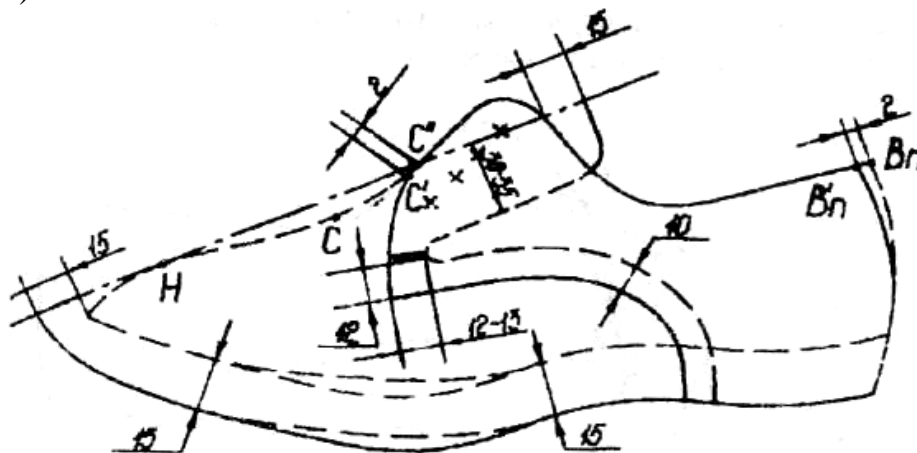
Побудова ґрунд-моделі макету заготовки
